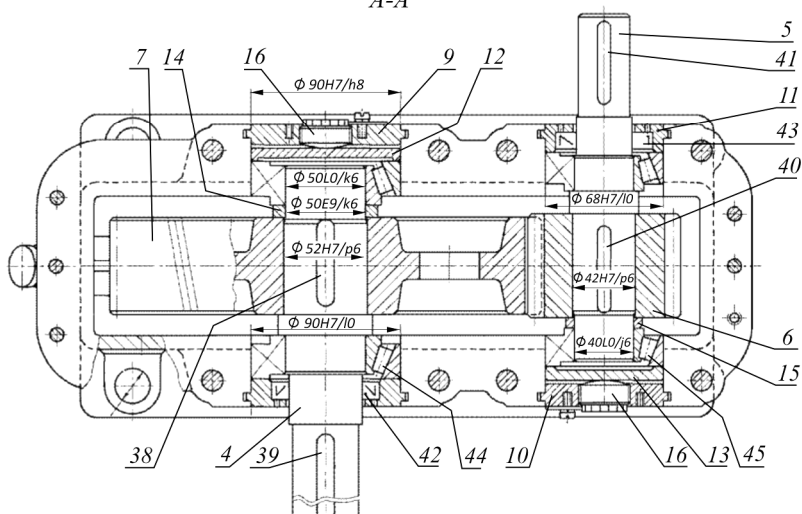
Редуктор цилиндрический одноступенчатый
